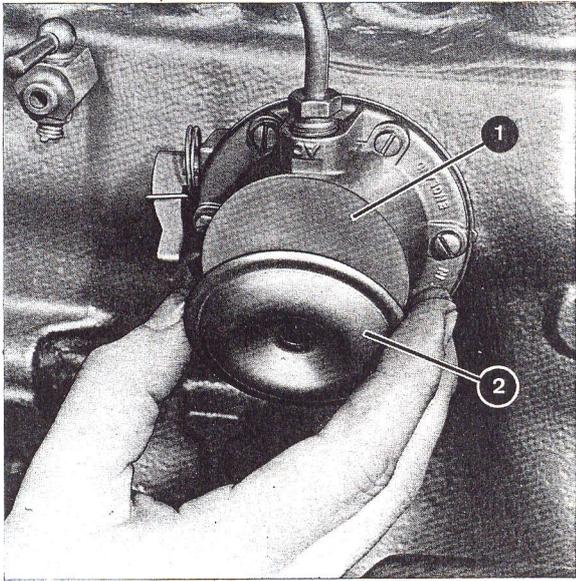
Dépose du couvercle de la pompe d'alimentation.
